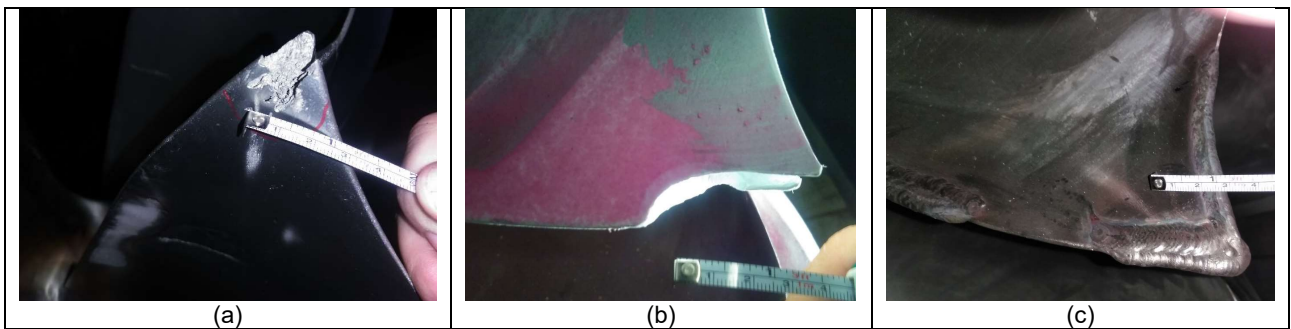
Septo da concha 5 – (a) perda de material, (b) após preparação para soldagem e (c) após soldagem em março de 2019.
